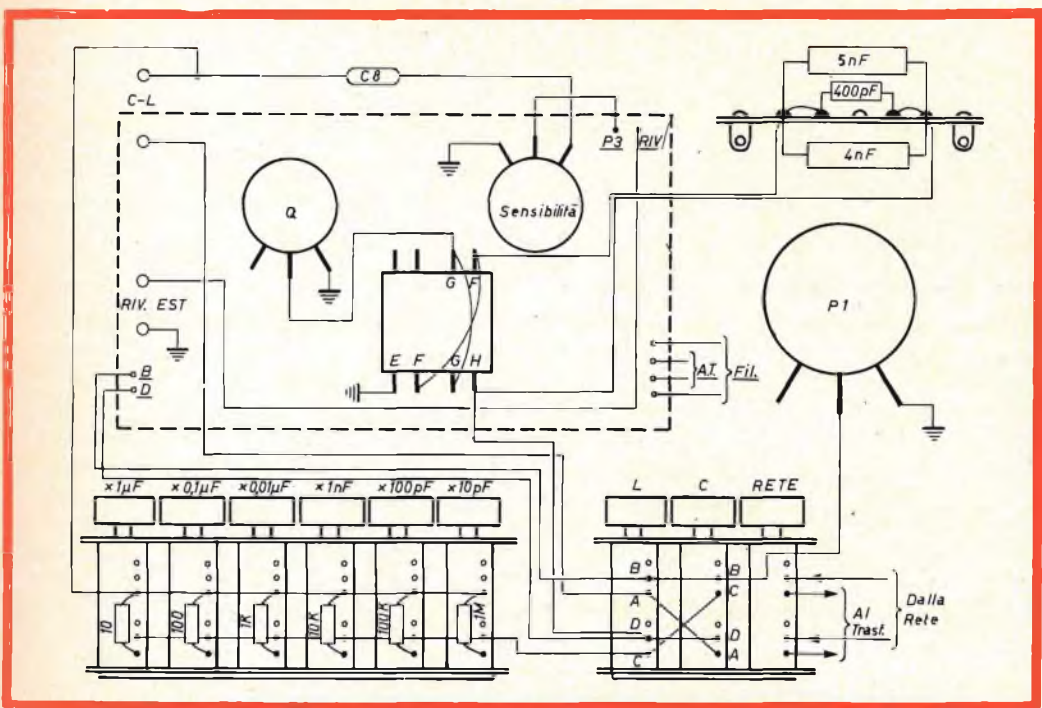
Collegamenti fra la piastra del circuito stampato e gli altri componenti montati sul pannello frontale.
